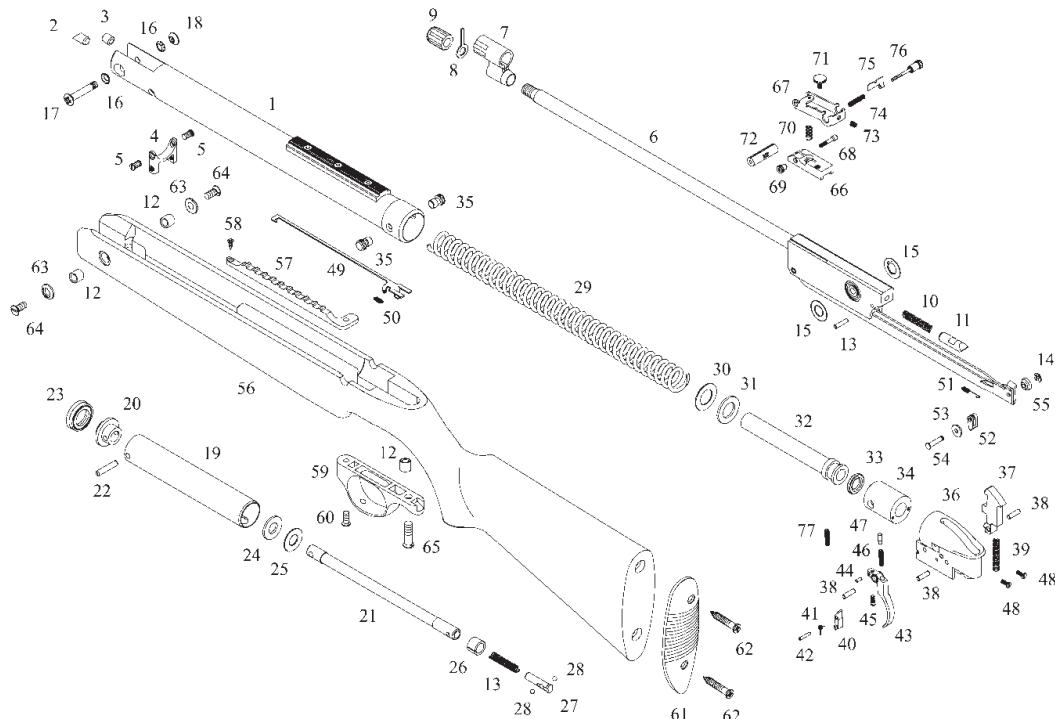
Сборочные единицы и детали винтовок MP-513М, MP-515, MP-515С
